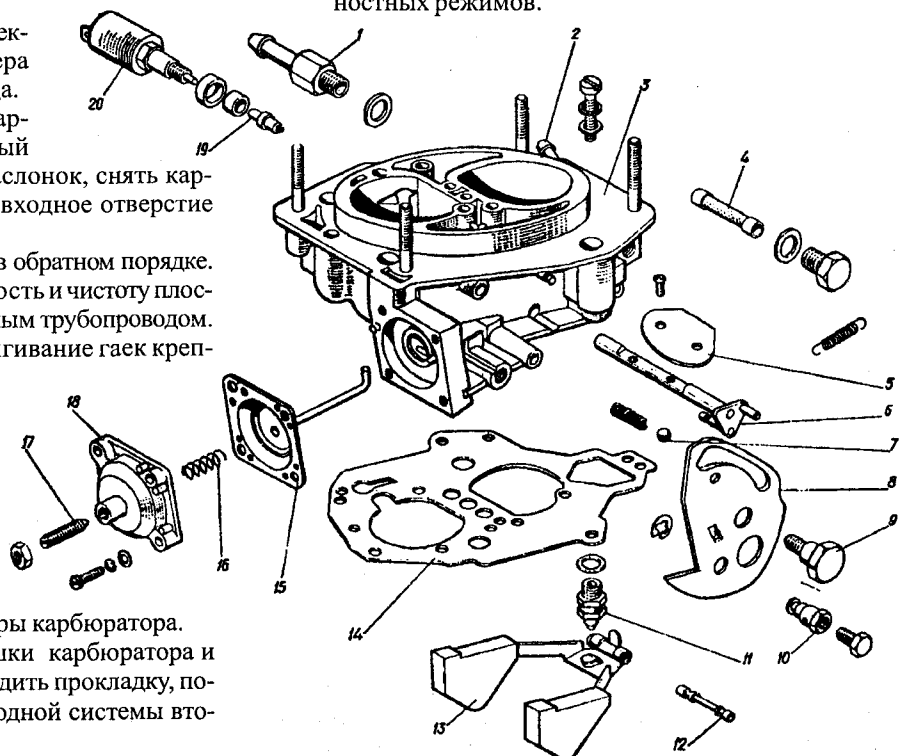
Детали крышки карбюратора: 1 – патрубок подачи топлива; 2 – патрубок слива топлива; 3 – крышка карбюратора; 4 – топливный фильтр; 5 – воздушная заслонка; 6 – ось воздушной заслонки с рычагом; 7 – шарик фиксации рычага управления воздушной заслонкой; 8 – рычаг управления воздушной заслонкой; 9 – ось рычага; 10 – втулка крепления тяги привода воздушной заслонки; 11 – игольчатый клапан; 12 – ось поплавка; 13 – поплавок; 14 – прокладка; 15 – диафрагма пускового устройства со штоком; 16 – пружина; 17 – регулировочный винт; 18 – крышка пускового устройства; 19 – топливный жиклёр холостого хода; 20 – электромагнитный запорный клапан
